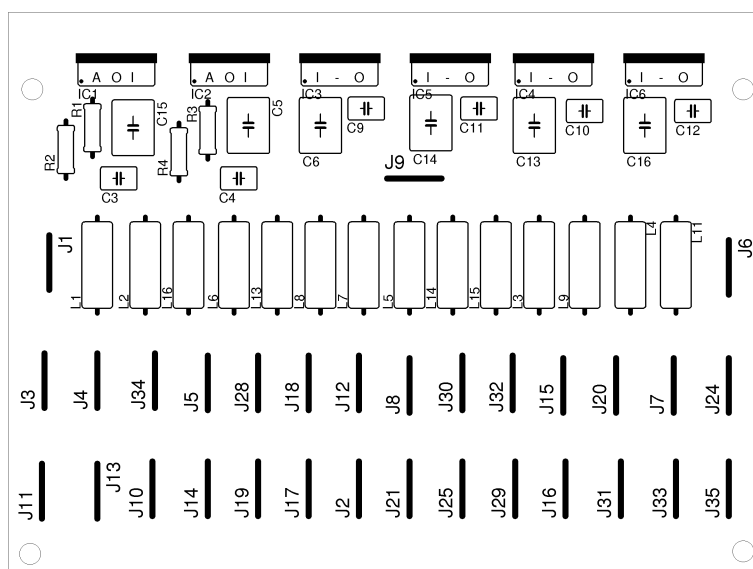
Schema zapojení bloku stabilizátorů
